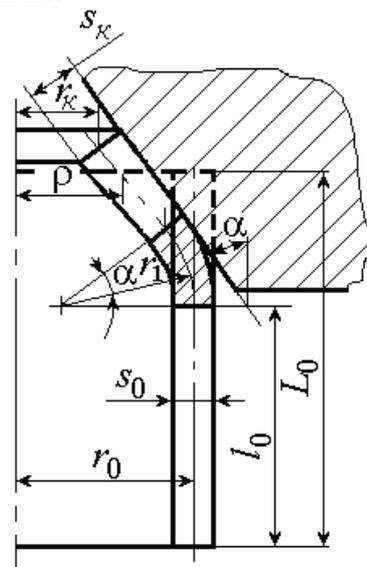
Схема обжима трубной заготовки в конической матрице
